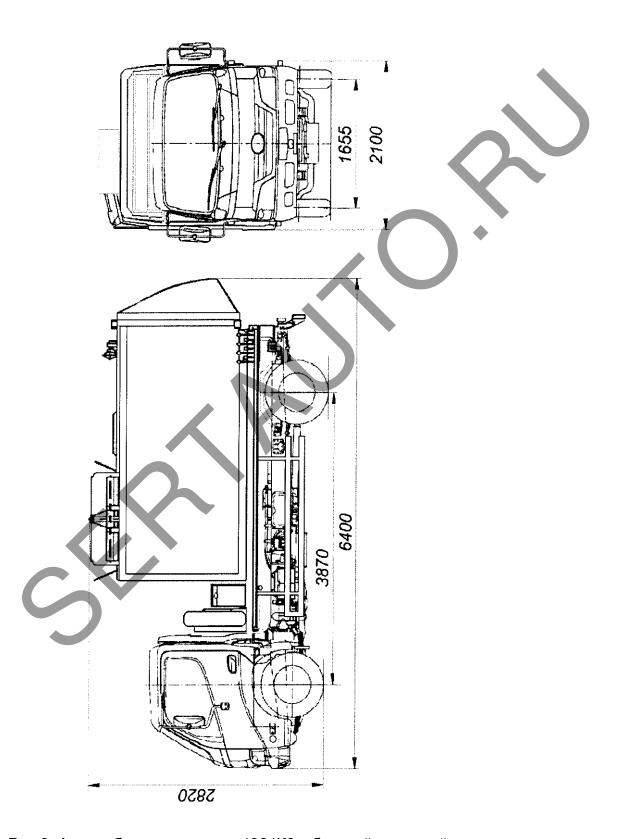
Автомобиль мусоровоз 4364К6 с боковой загрузкой
